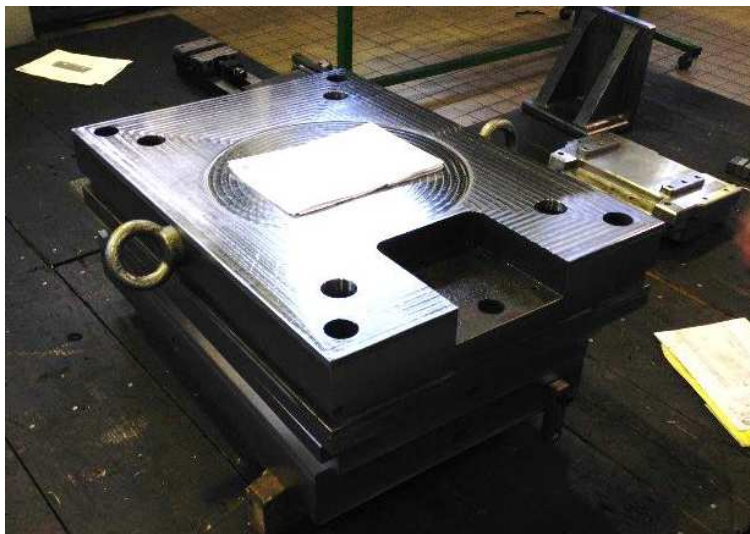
cavidade do molde de injeção (parte fixa do molde).
